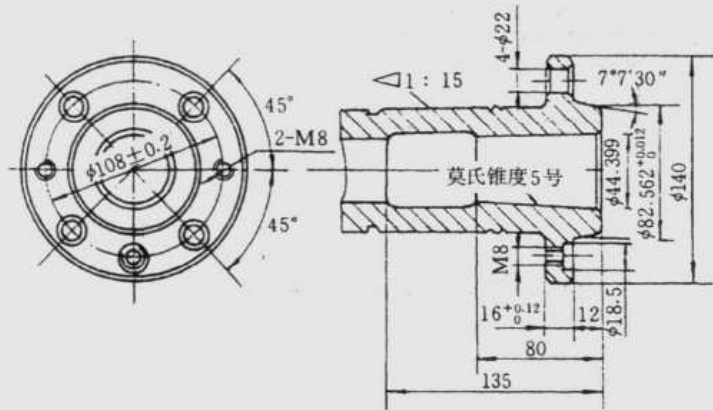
CA6132A、C6140A、C6232A、C6240A 主轴尺寸
